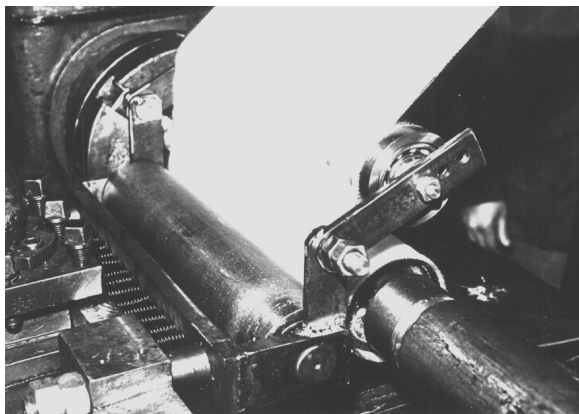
Уплотнение трубчатой заготовки прикаточным роликом
